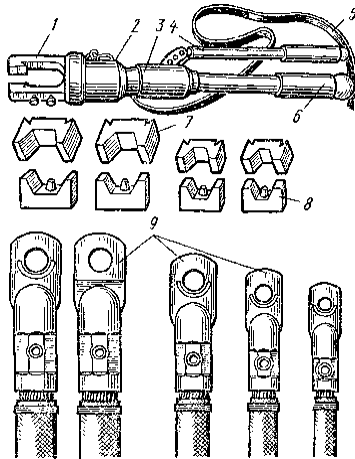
Ручний гідравлічний прес ПГР-20М1:
